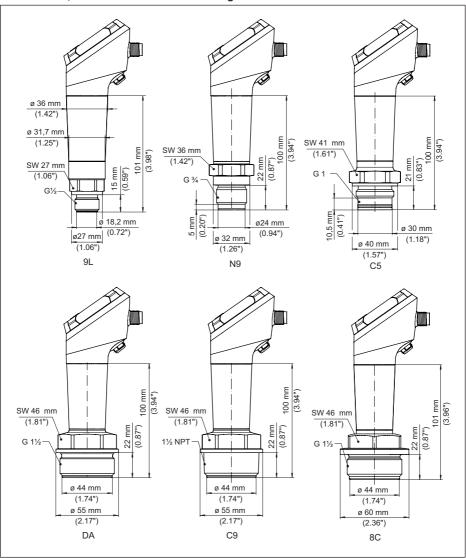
VEGABAR 38, Gewindeanschluss frontbündig
